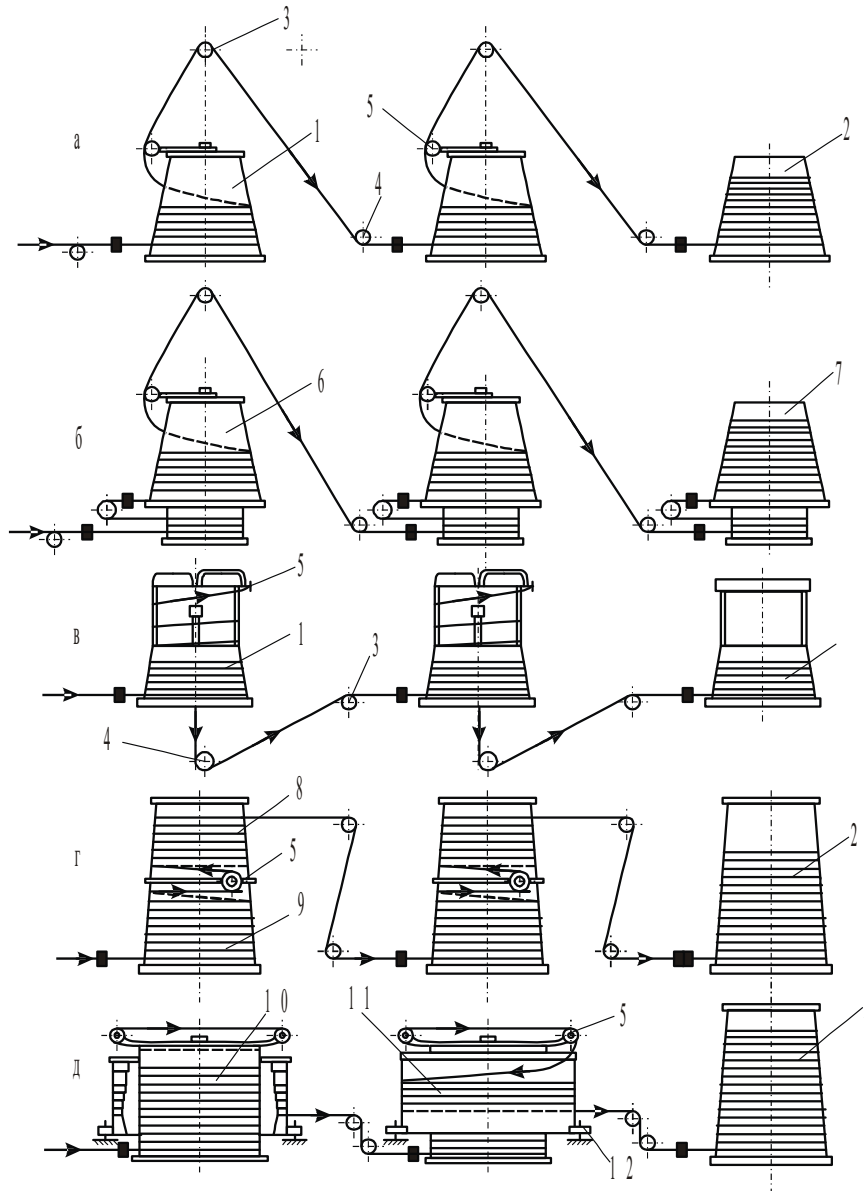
Схеми машин багаторазового волочіння магазинного типу: а - з одинарними барабанами звичайного типу: б – із двоступінчастими барабанами: в – з барабанами, що мають внутрішній порожній вал для проводки дроту; г- зі здвоєними двох'ярусними барабанами: д – зі здвоєними зовнішніми й внутрішніми барабанами; 1 – проміжний барабан; 2 – чистовий барабан; 3- напрямний ролик; 4 – низький напрямний ролик; 5 – повідковий пристрій; 6 – проміжний двоступінчастий двоступеневий барабан; 7 – чистовий
